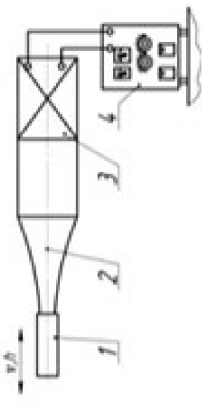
Вібратор з коливальним, що здійснює обертовий рух (0,01-0,02 Гц).
